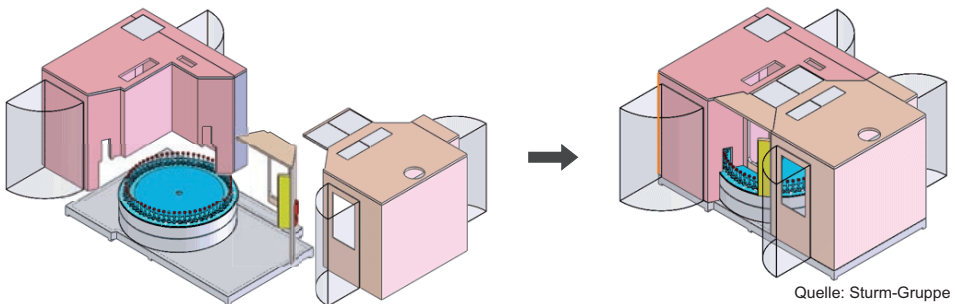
Beispiel: Layout-Konzept einer Beschichtungsanlage
